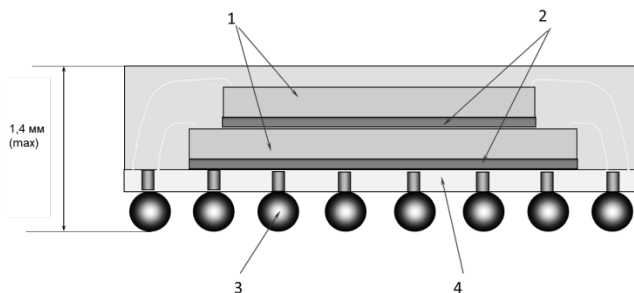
Конструкция ИС в корпусе *CSP*:
